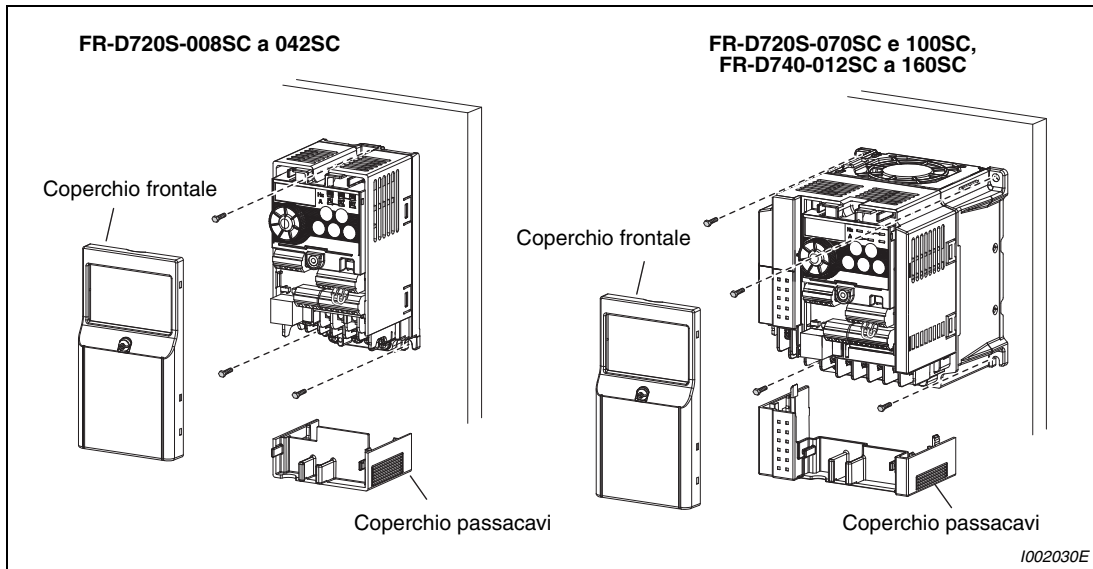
Installazione sul pannello di montaggio di un armadio elettrico
